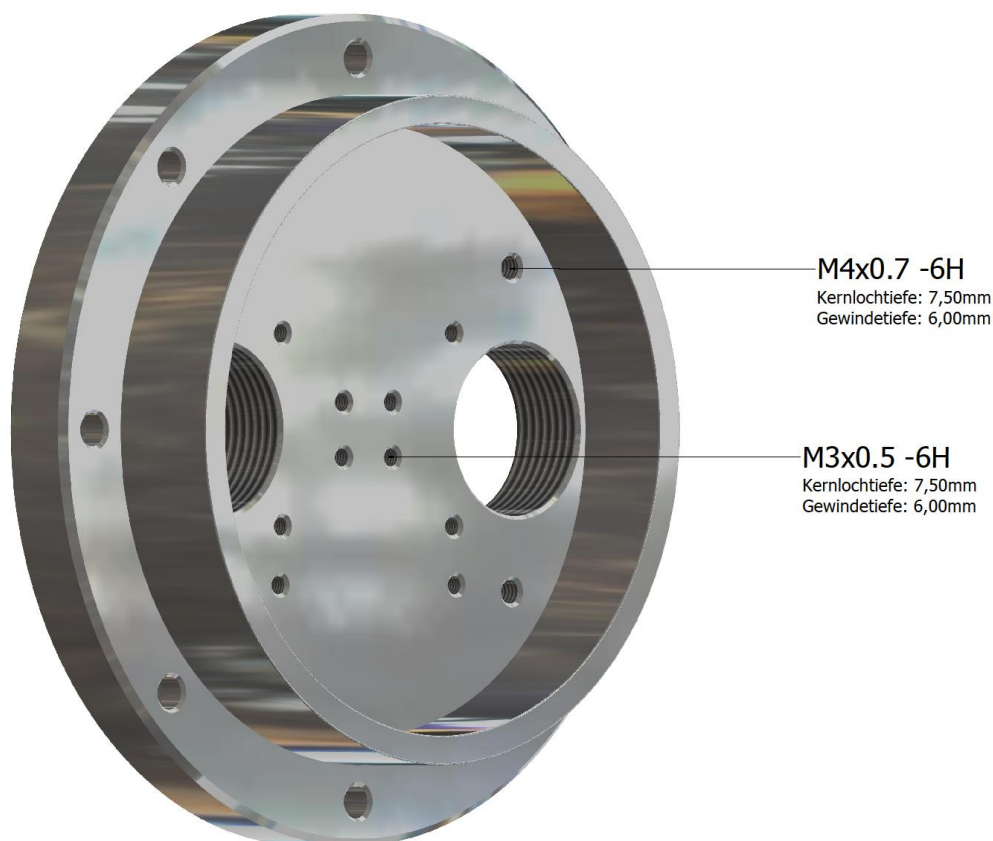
Beispiel Gewinde-Sacklöcher zur Montage
